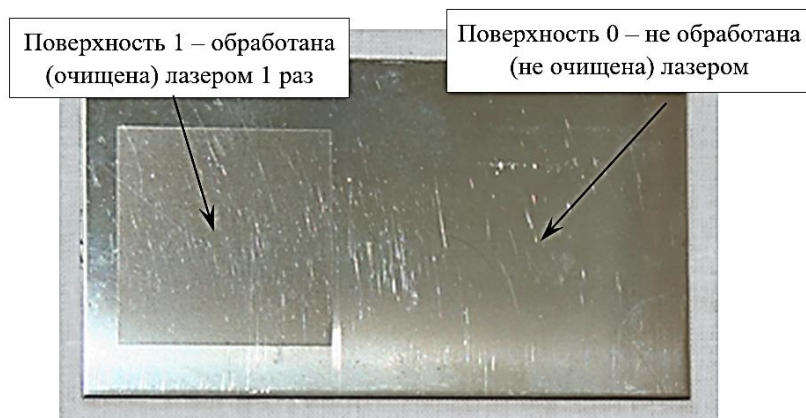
Фотография образца Б (высокое качество поверхности – «зеркало»)
